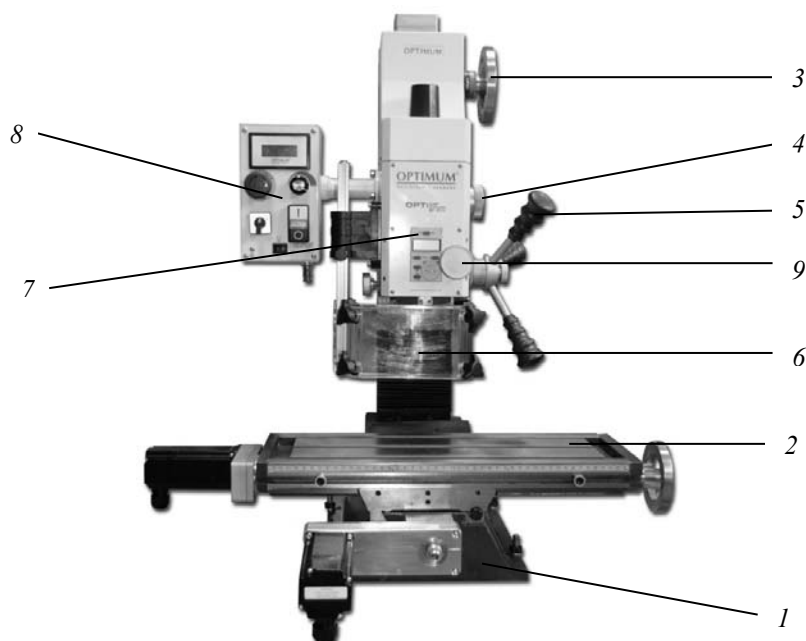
Общий вид фрезерного станка модели Optimum BF20 Vario
